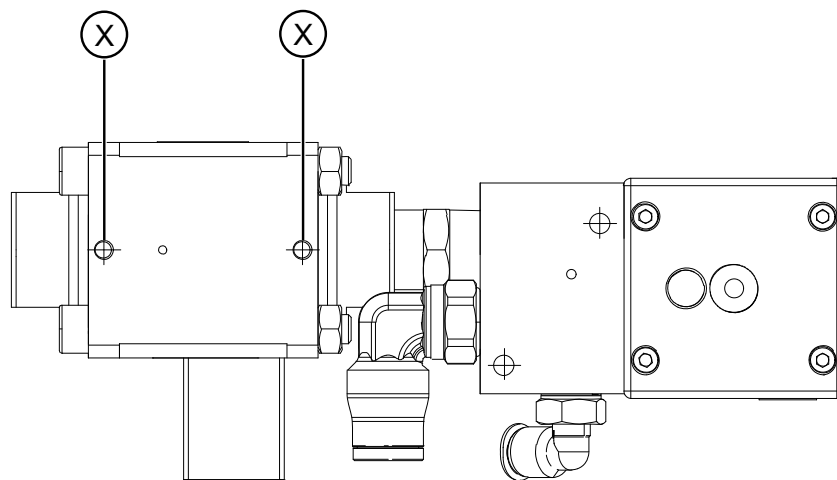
1-Gas-Ausführung, Befestigung Schaltventil (optional), Gewinde M4
